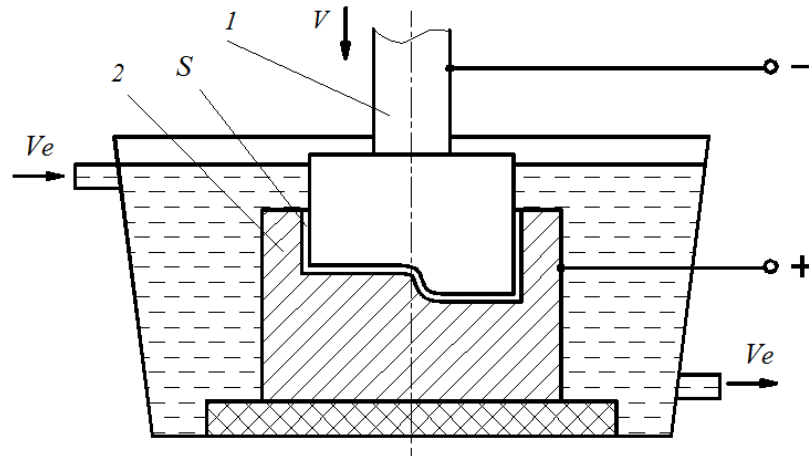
Схема прошивання (1 – інструмент копір; 2 – заготовка)
